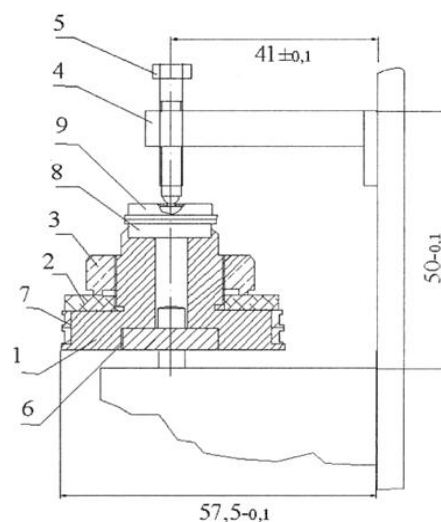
Конструкция устройства для лазерной сварки кольцевых швов корпусов ДА на установке «Квант-15»
